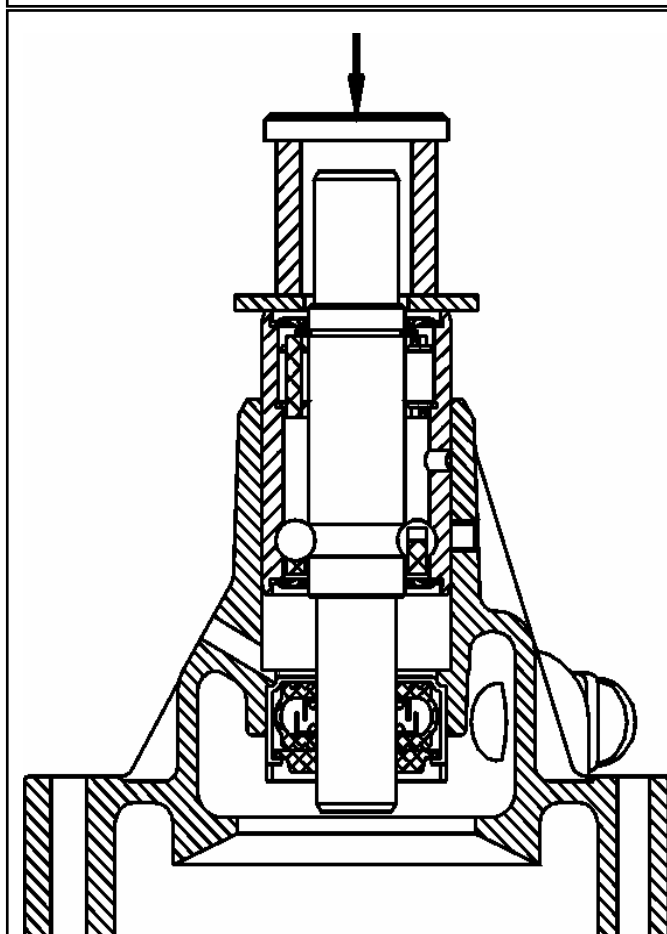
Запрессовка подшипника с валиком в сборе в корпус насоса
